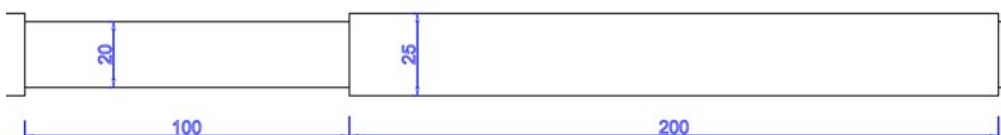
Particolare dei restringimenti di sezione delle aste (le misure sono espresse in mm).
